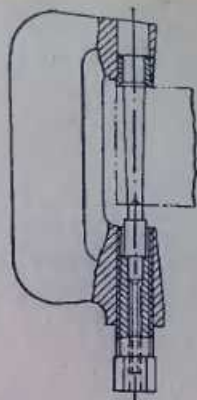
Струбцина ЛМ9690-060 для выпрессовки и запрессовки конического штифта шатуна
